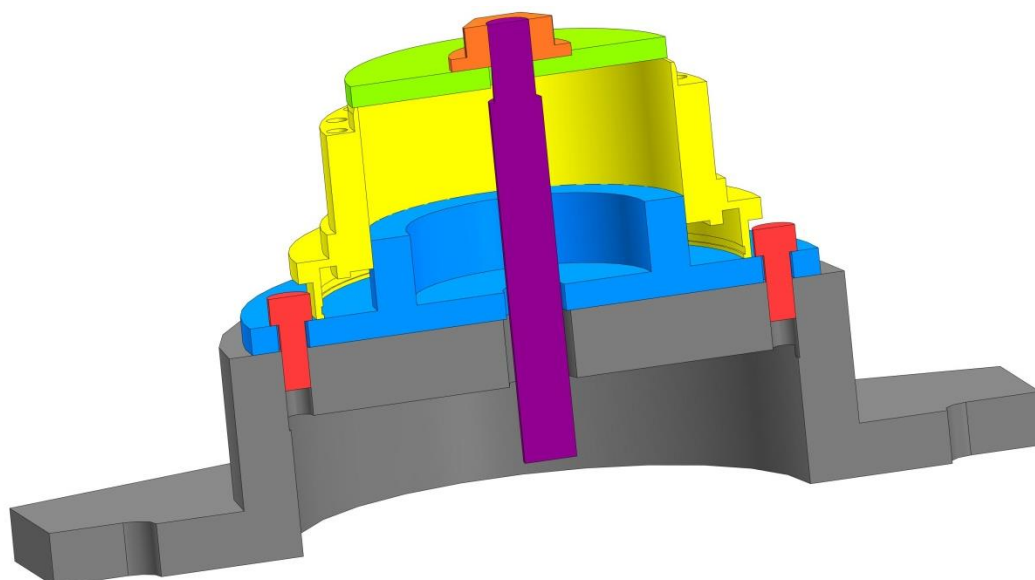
Спроектований верстатний пристрій та закріплена деталь у розрізі
